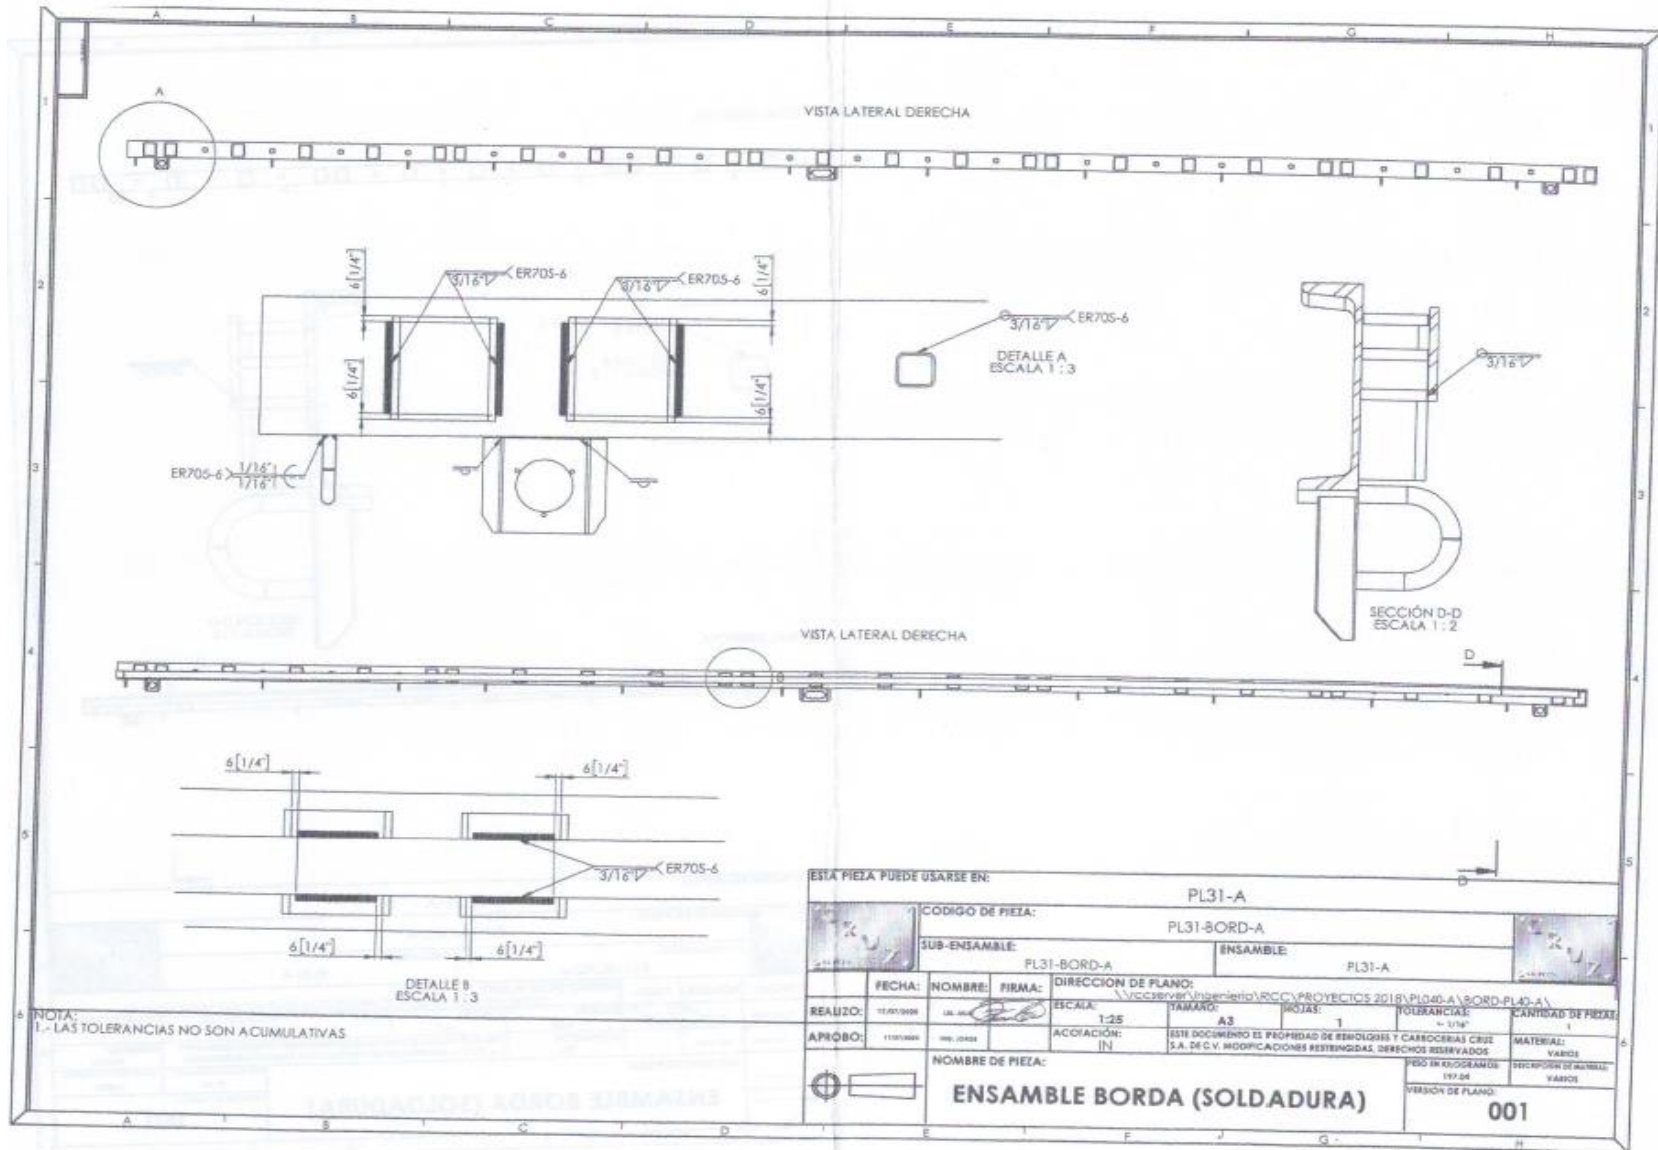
Plano del ensamble de borda (soldadura). Fuente: Remolques y Carrocerías Cruz, S.A. de C.V., 2020.
